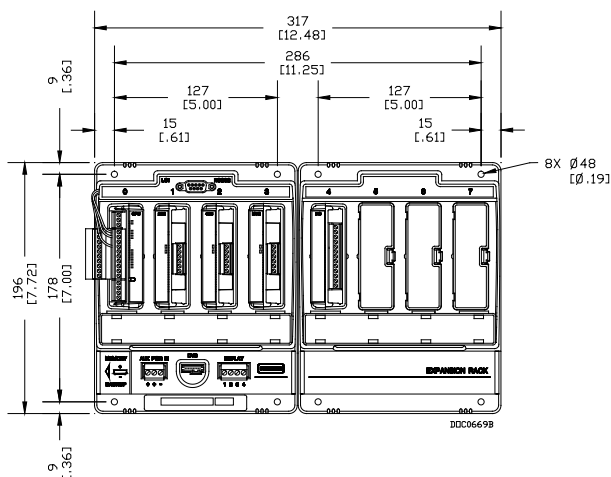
Dimensioni dell'FB107 e del rack di espansione
